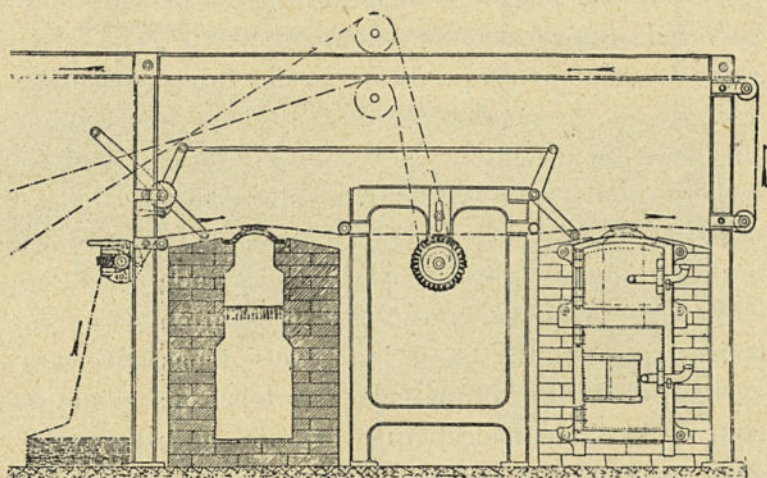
Coupe d'une grilleuse chauffée au charbon
